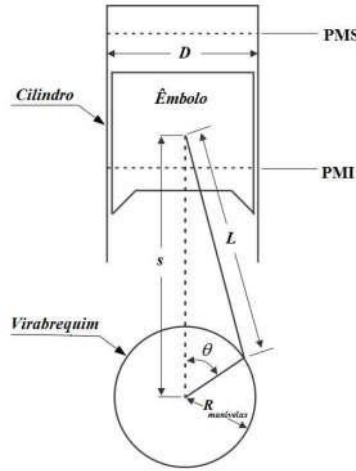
Corte esquemático de um cilindro de um motor Diesel.
